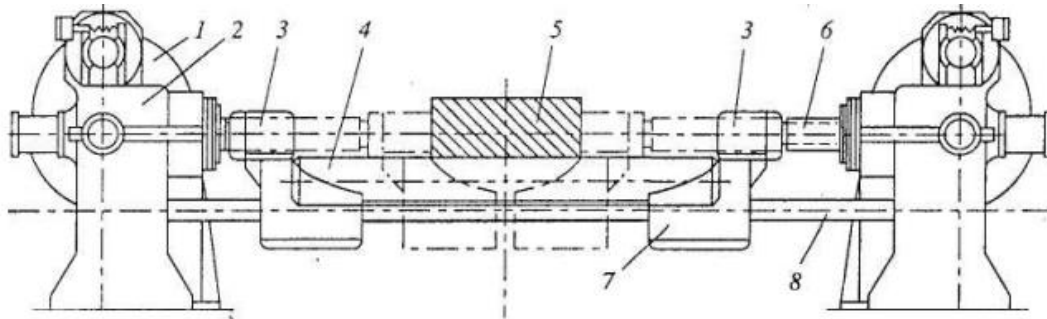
Маніпулятор стану 2800: 1 - двигун; 2 - черв'ячний редуктор; 3 - лінійки; 4 - рольганг; 5 - сляб; 6 - гвинти; 7 - повзуни лінійок; 8 -напрямні штанги
